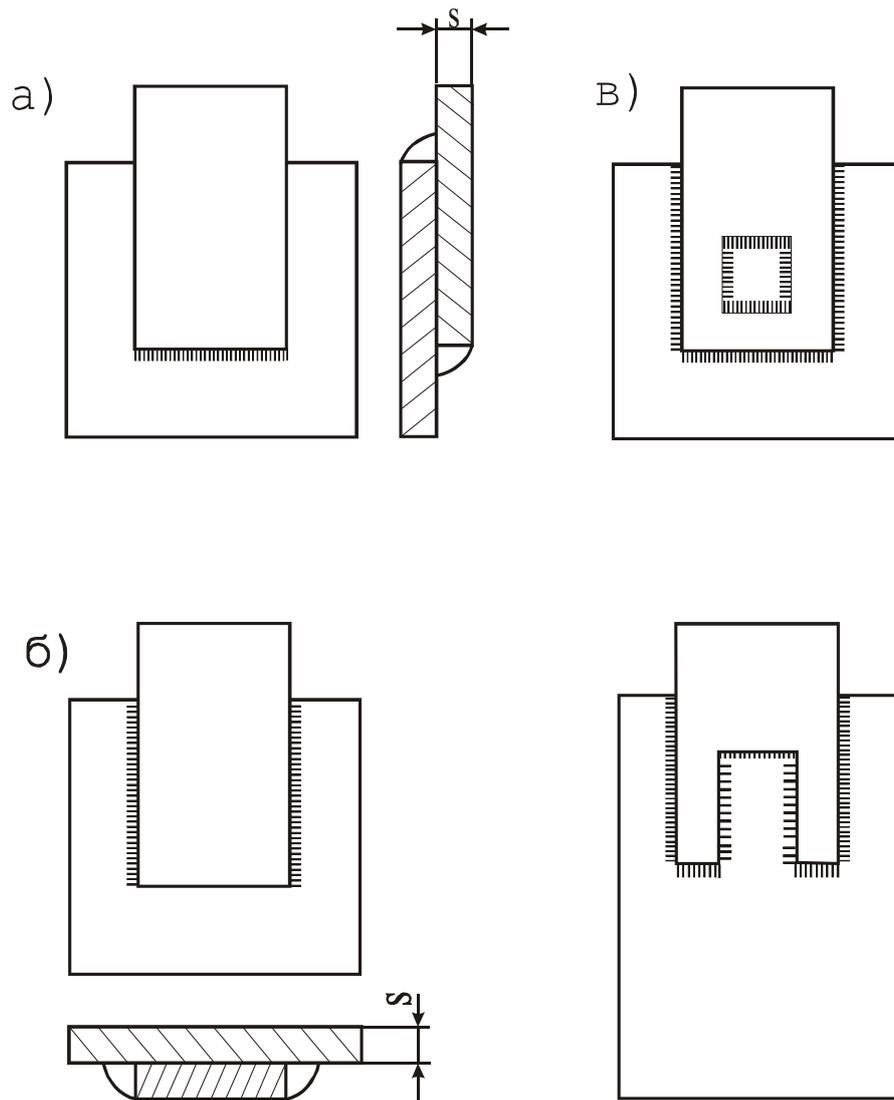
Виды нахлесточных сварных соединений: а- с лобовыми швами; б- с фланговыми швами; в- прорезные.
